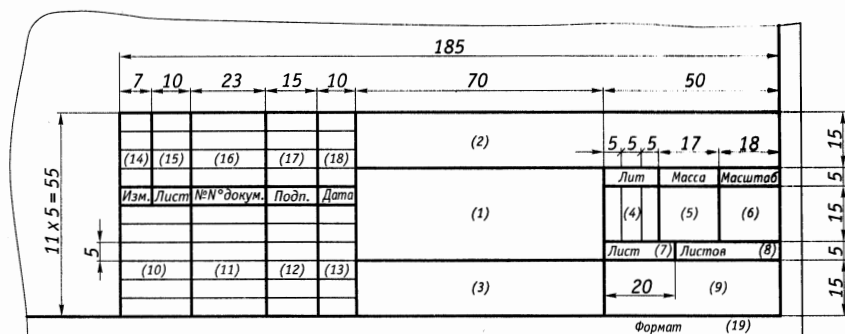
Размеры и форма основной надписи для чертежей:
